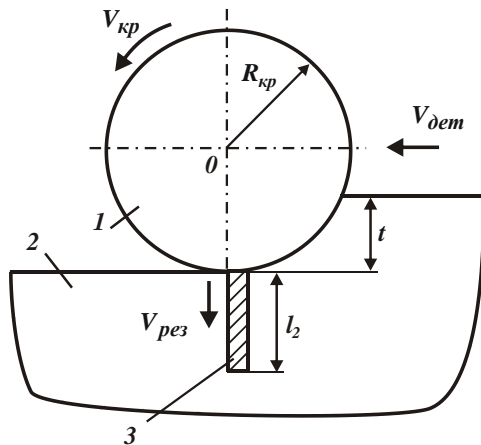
Расчетная схема параметров процесса плоского шлифовании: 1 – шлифовальный круг; 2 – обрабатываемая деталь; 3 – адиабатический стержень
